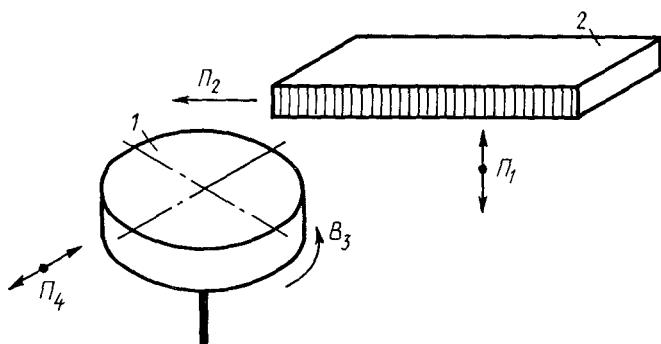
Способ обработки зубчатого колеса длинной зуборезной гребенкой
